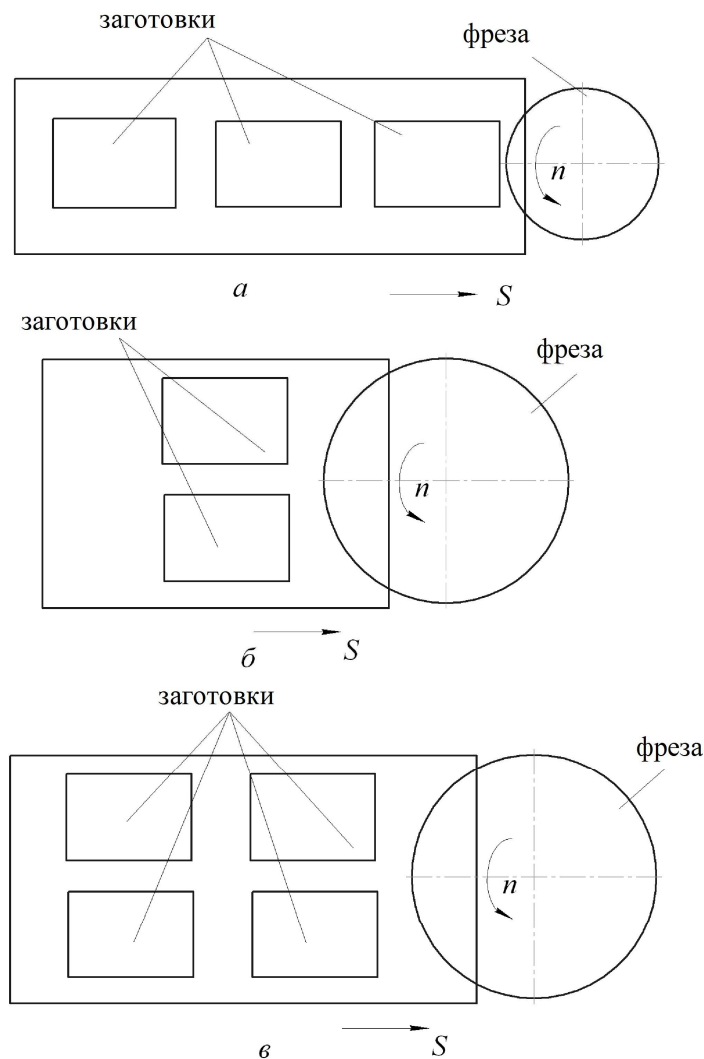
Способы установки деталей на вертикально-фрезерном станке (вид сверху на стол)
